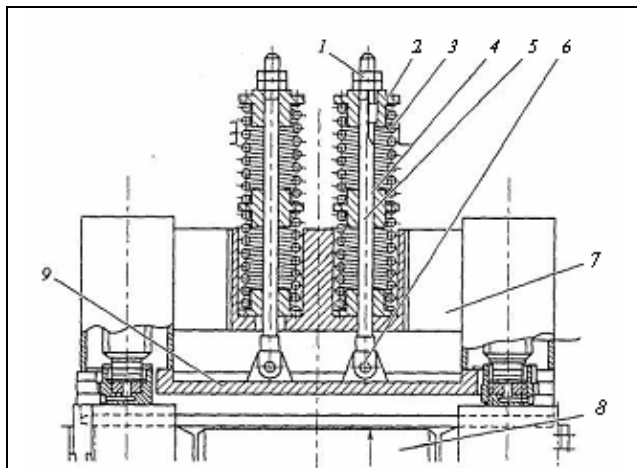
Пружинное уравнивание валка стана 530: 1-гайка; 2-втулка; 3-пружина; 4- втулка; 5-шток; 6-узел крепления к траверсе; 7-верхняя траверса
